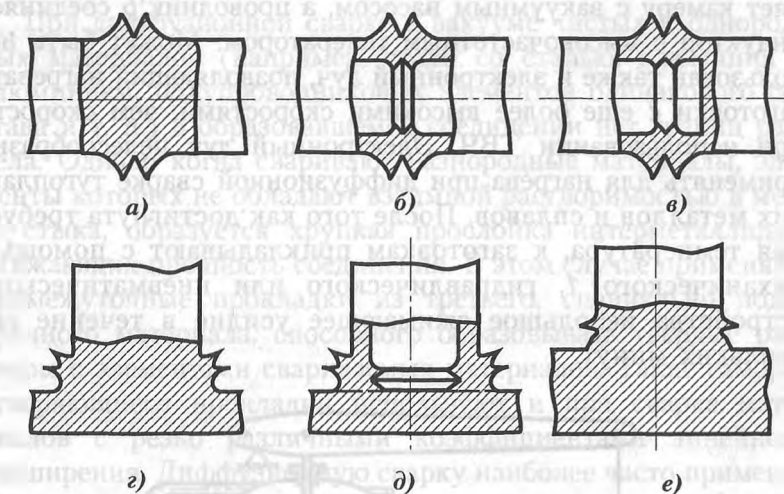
Типы сварных соединений сварки трением: а — стержней встык; б — труб встык; в — встык стержня с трубой; г — стержня с листом; д — трубы с листом; е — стержня с массивной деталью
